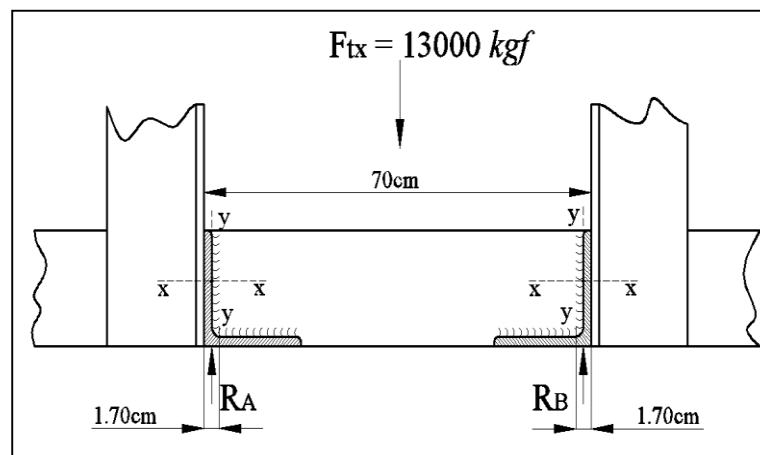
34 Momento flector en la soldadura de la base
